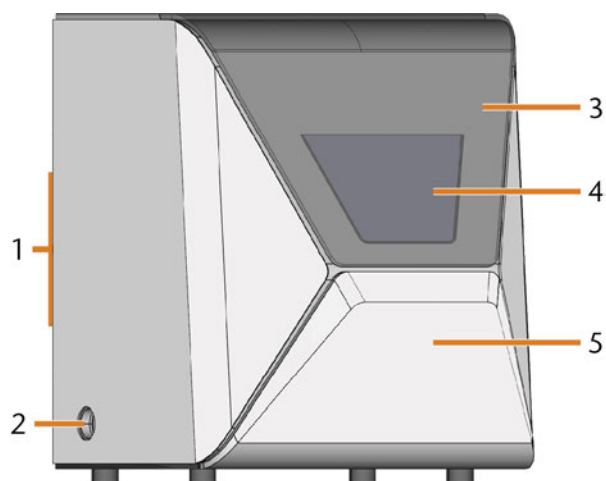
VISTA FRONTAL DE LA MÁQUINA
